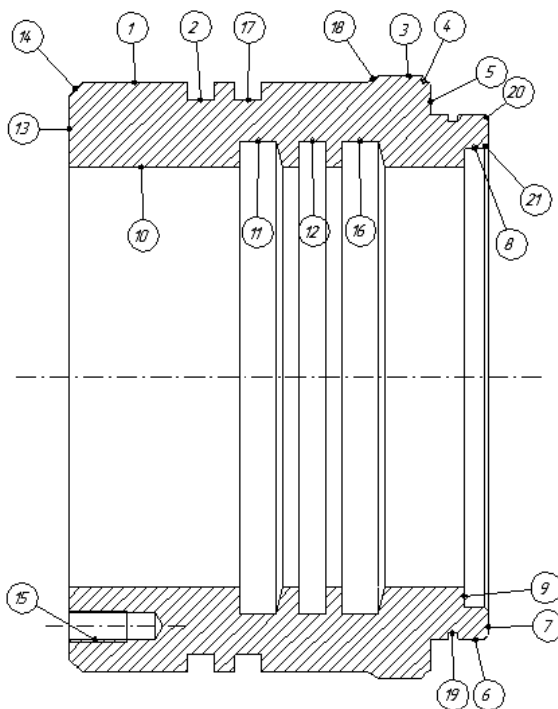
Эскиз детали Втулка домкрата с обозначением поверхностей
